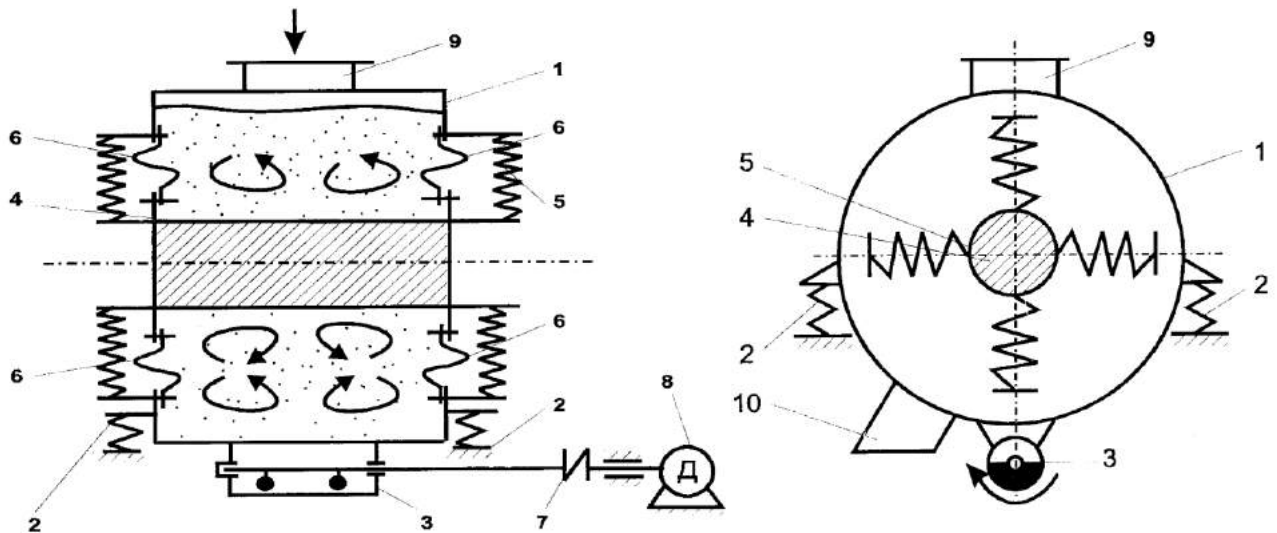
Схема вібраційної машини з інерційним активатором руху робочого середовища: 1 – робоча камера; 2 – пружні опори; 3 – дебалансний вібробуджувач; 4 – активатор; 5 – пружна підвіска; 6 – еластичні стінки; 7 – еластична муфта; 8 – двигун; 9 – завантажувальна горловина; 10 – вивантажувальна горловина
